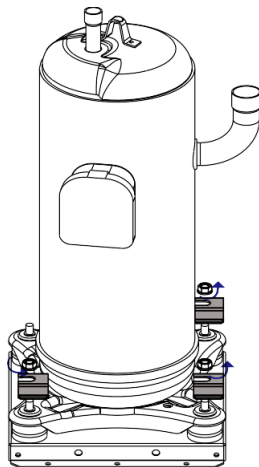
Снятие неподвижных деталей компрессора из листового металла
